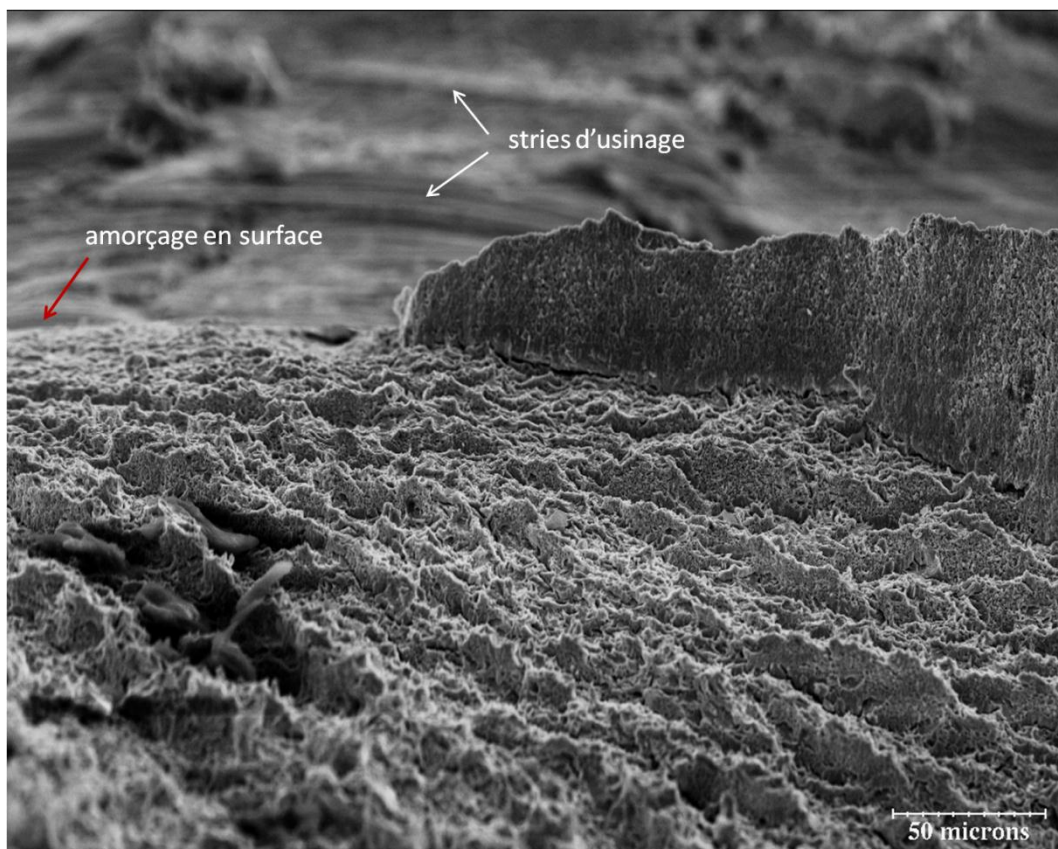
Amorçage de la rupture en surface à partir d'un défaut d'usinage sur une éprouvette de type AE-R2 testée à -120°C .
